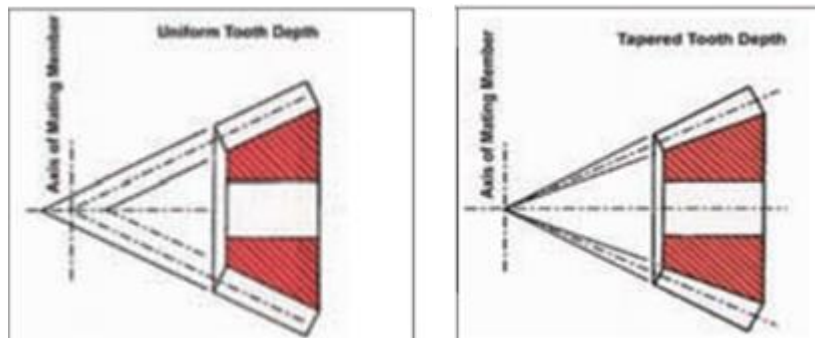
a) Engranaje espiro-cónico con espesor de dientes constante b) Engranaje espiro-cónico con espesor de dientes variable Fuente: [7]
